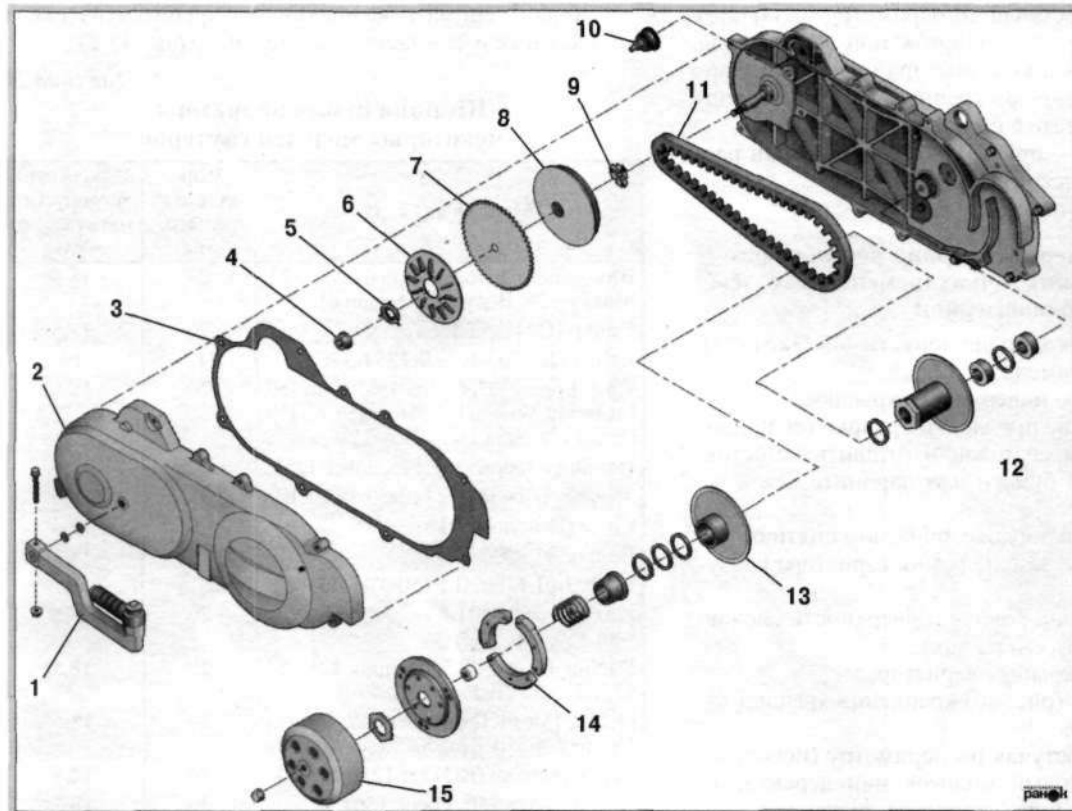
Детали вариатора: 1 – рычаг кик-стартера; 2 – крышка вариатора; 3 – прокладка вариатора; 4 – гайка ведущего шкива; 5 – шайба; 6 – крыльчатка; 7 – шкив привода кик-стартера; 8 – ведущий диск вариатора в сборе; 9 – втулка; 10 – обгонная муфта стартера; 11 – ремень вариатора; 12 – внутренняя половина ведомого шкива; 13 – наружная половина ведомого шкива; 14 – колодки сцепления; 15 – корпус сцепления
